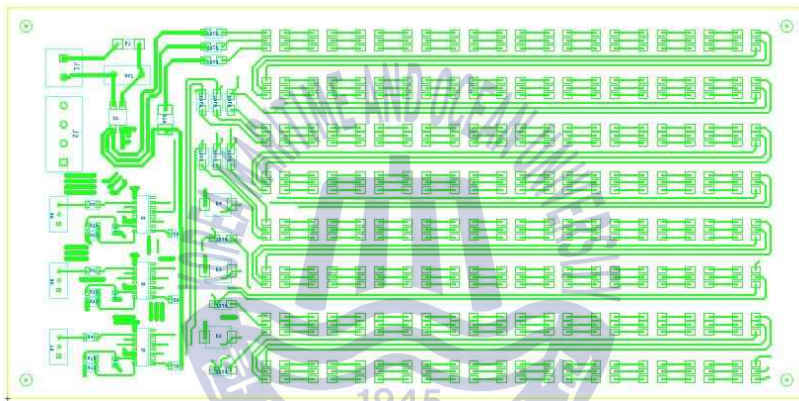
220[VAC] RGB LED 보드 PCB 레이아웃
